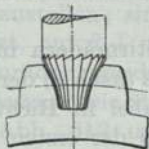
Fräsen der Stirnräder mit dem Kopfräser.
